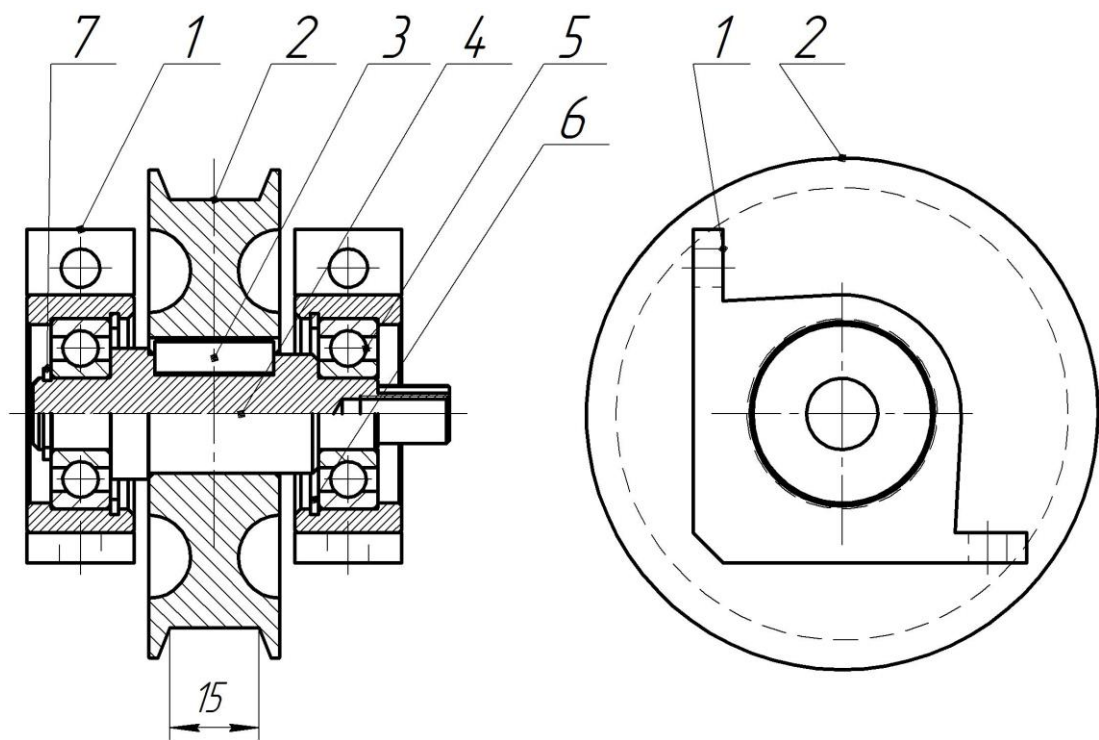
Опорне колесо вантажного візка з привідним валом та буксами: 1 – букса – підшипникова опора; 2 – ходове колесо; 3 – шпонка; 4 – вал привідний; 5 – підшипник; 6, 7 – кільце стопорне.
